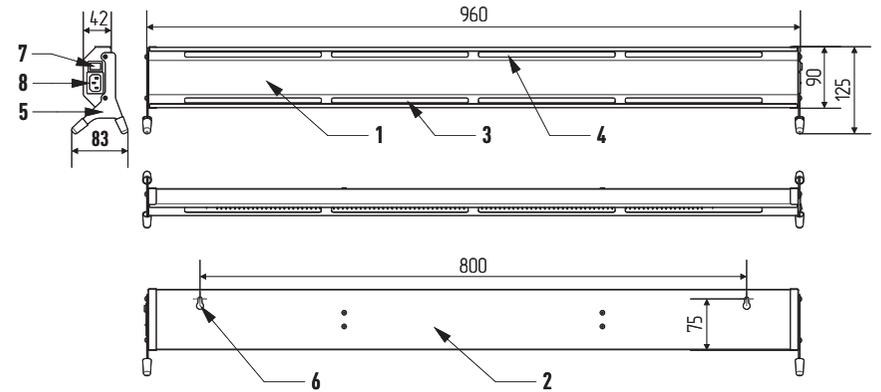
Габаритный чертеж и элементы конструкции электрического обогревателя.
